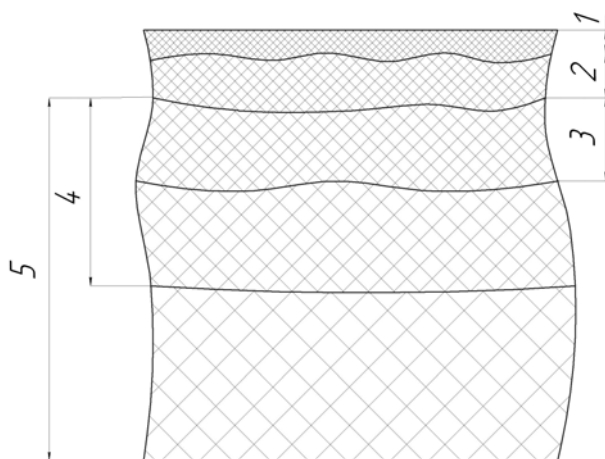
Схематичне розташування зон поверхневого шару, після електроерозійної обробки
